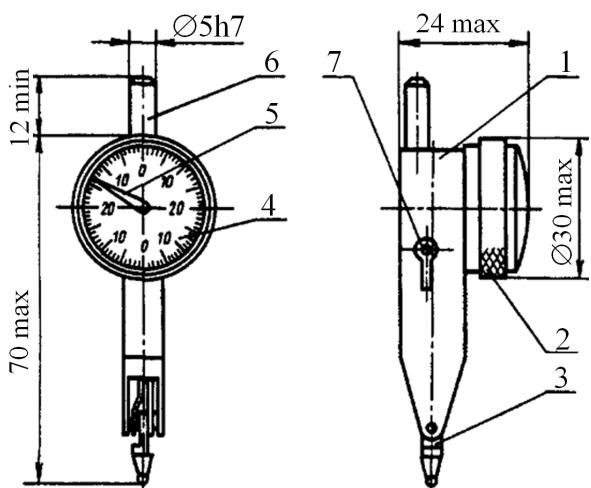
Внешний вид и основные размеры рычажно-зубчатых индикаторов типа ИРБ:
